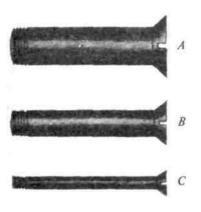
Стальные винты для запорных пластин, винт для спускового механизма и винт для вращающейся гайки
